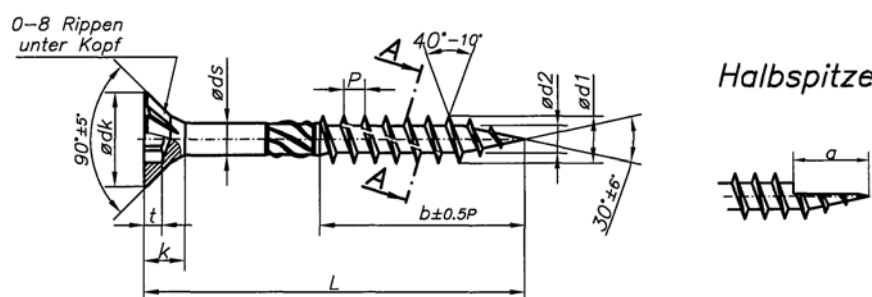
Skizze der Holzbauschraube „Star Drive“ [34]
